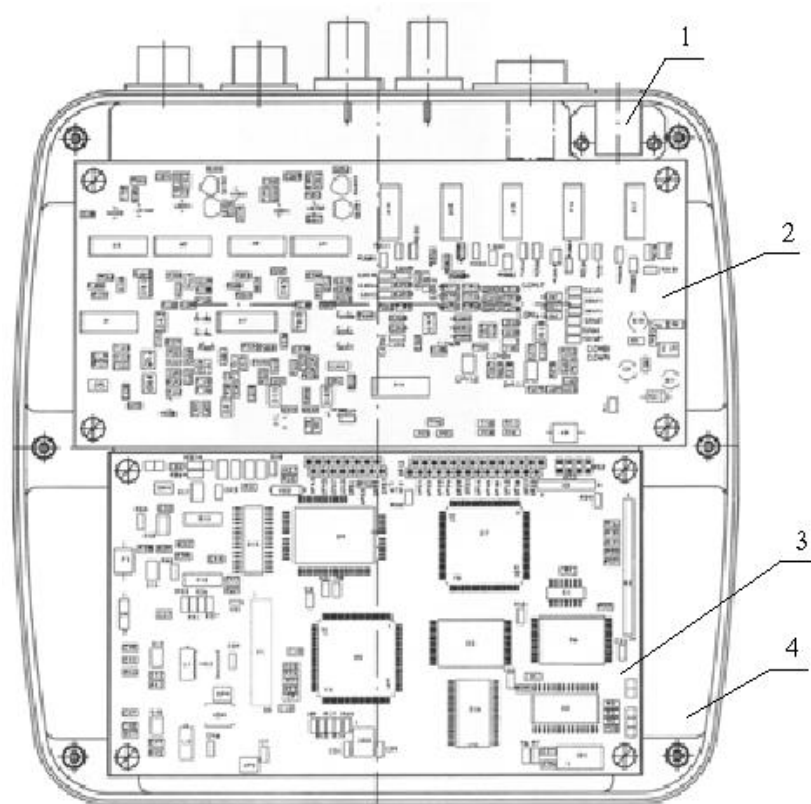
Общий вид расположения плат прибора АДП-3101:
